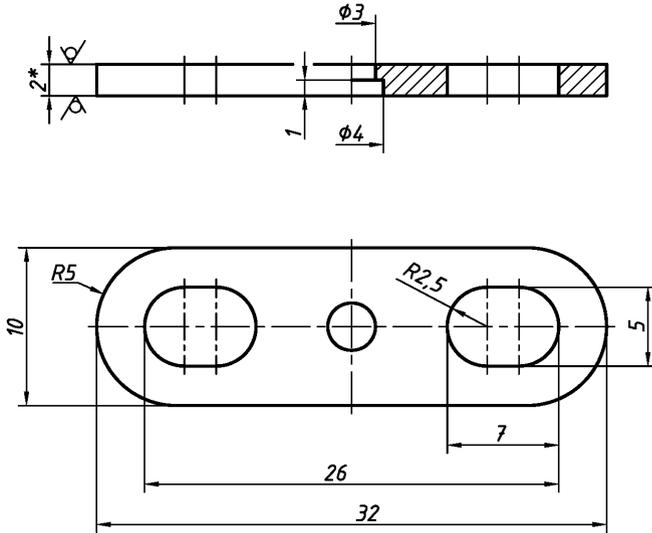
Оформление рабочего чертежа сборочной единицы «Опора подшипника», образованной расклепкой
